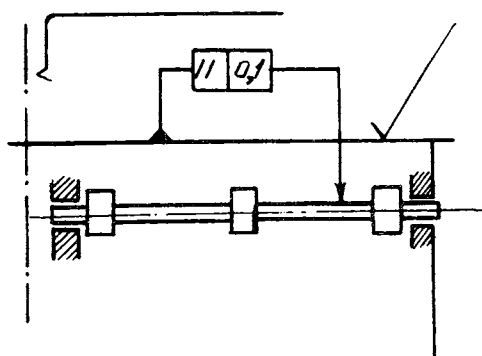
Exemplu de toleranță de poziție din mașina de perforat Soemtron 415.
